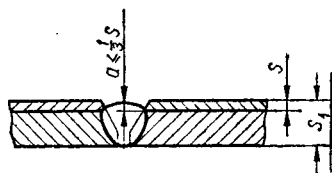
Схема подготовки кромок для сварки в двухслойных сталях.
